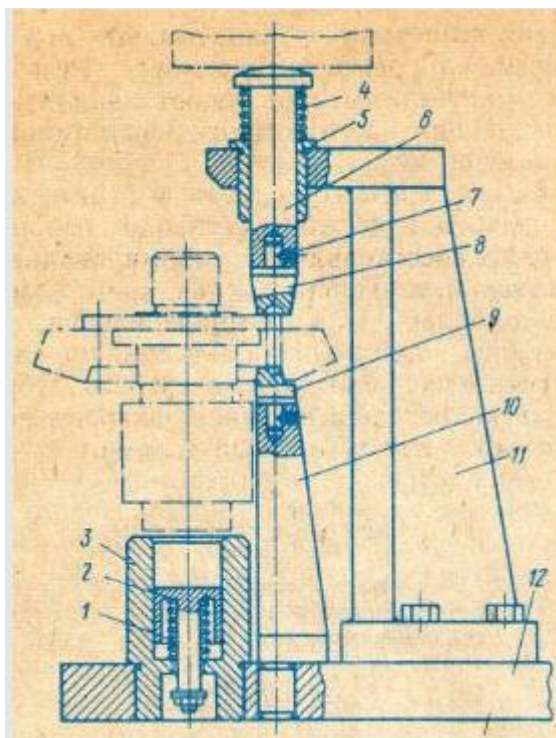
Приспособление для клепки ведущей цилиндрической и ведомой конической шестерни
